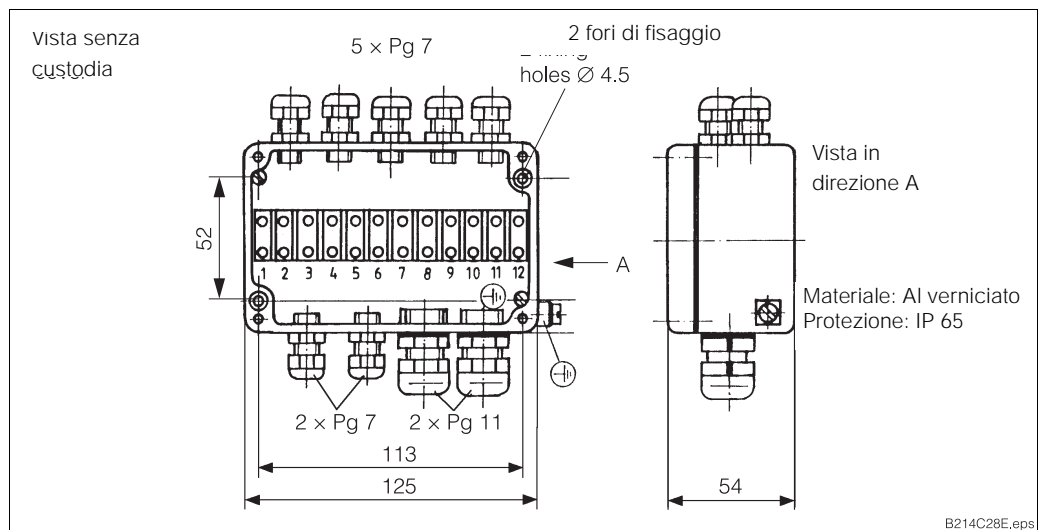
Cassetta di collegamento VBC con messa a terra; dimensioni: 125 x 80 x 54 mm (l x h x d)
